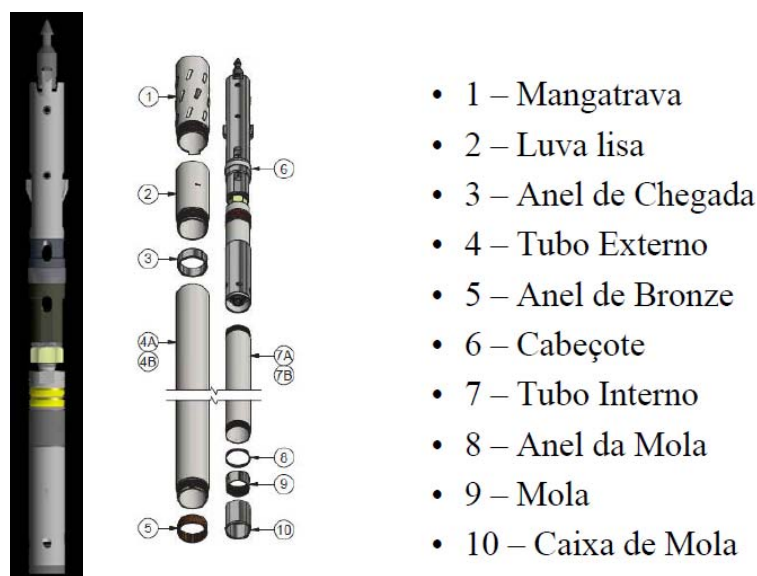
Barrilete wireline montado e explodido. Modificado de <http://www.atlascopco.com/usus/products/drilling-tools/1528804>
